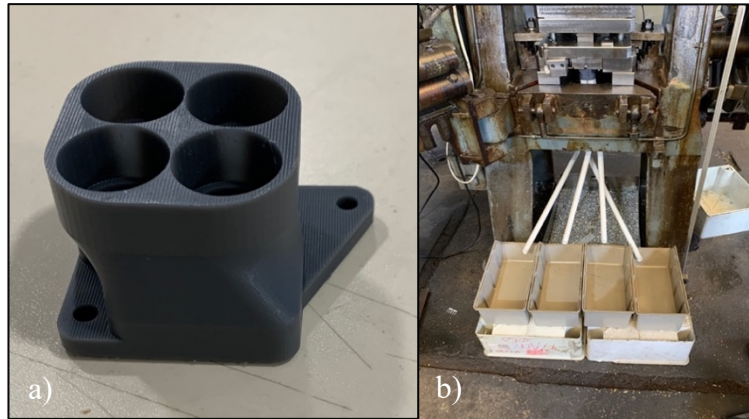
Separador de peças: a) Separador impresso em impressora 3D;
